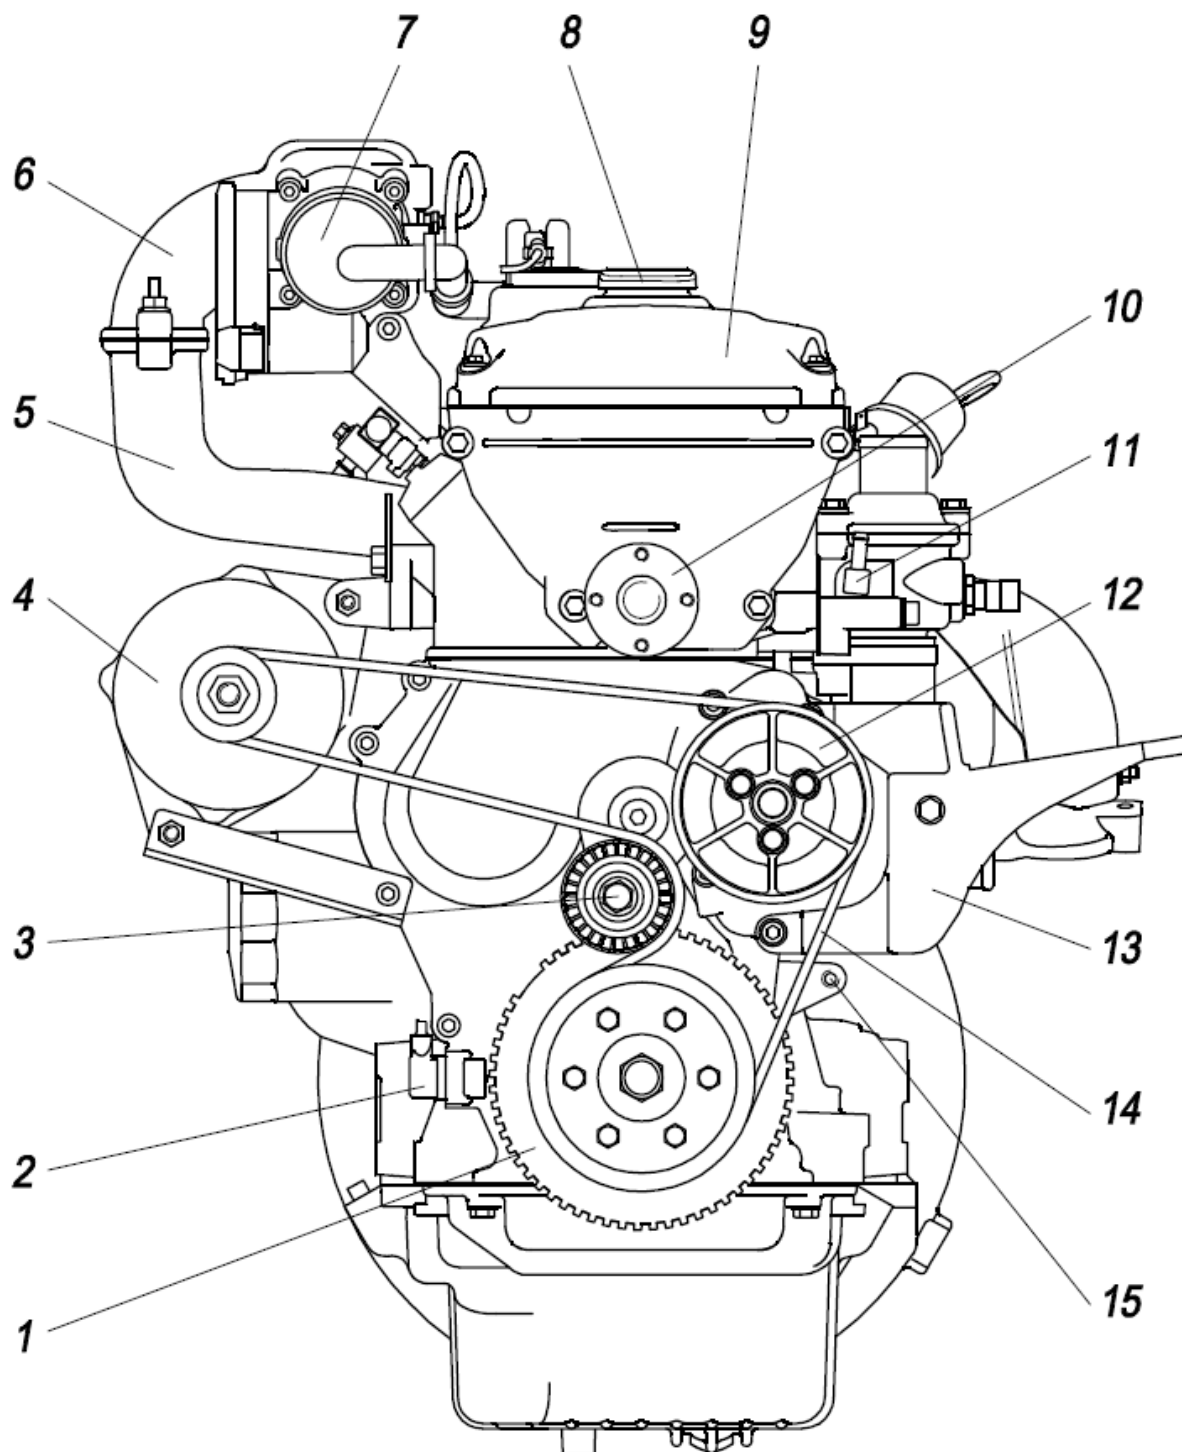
Вид спереди двигателя ЗМЗ-40904.10:
